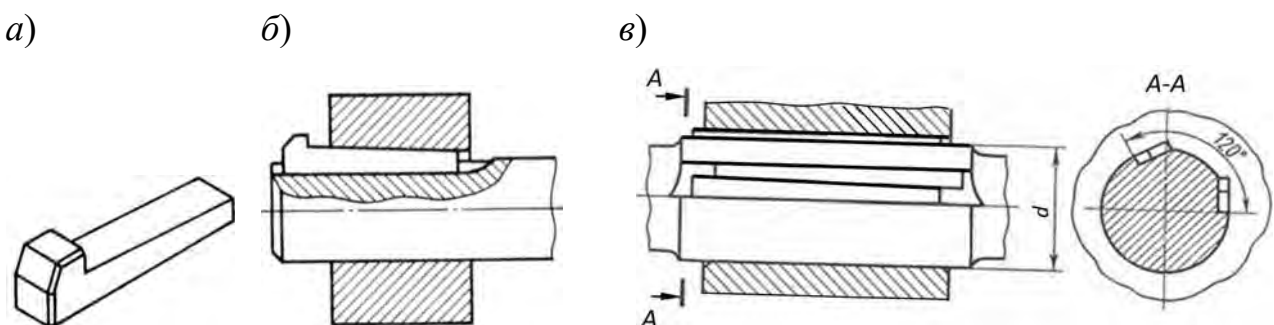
Напряженные шпоночные соединения: а – клиновая шпонка; б – схема соединения клиновой шпонкой; в – схема соединения тангенциальными шпонками
